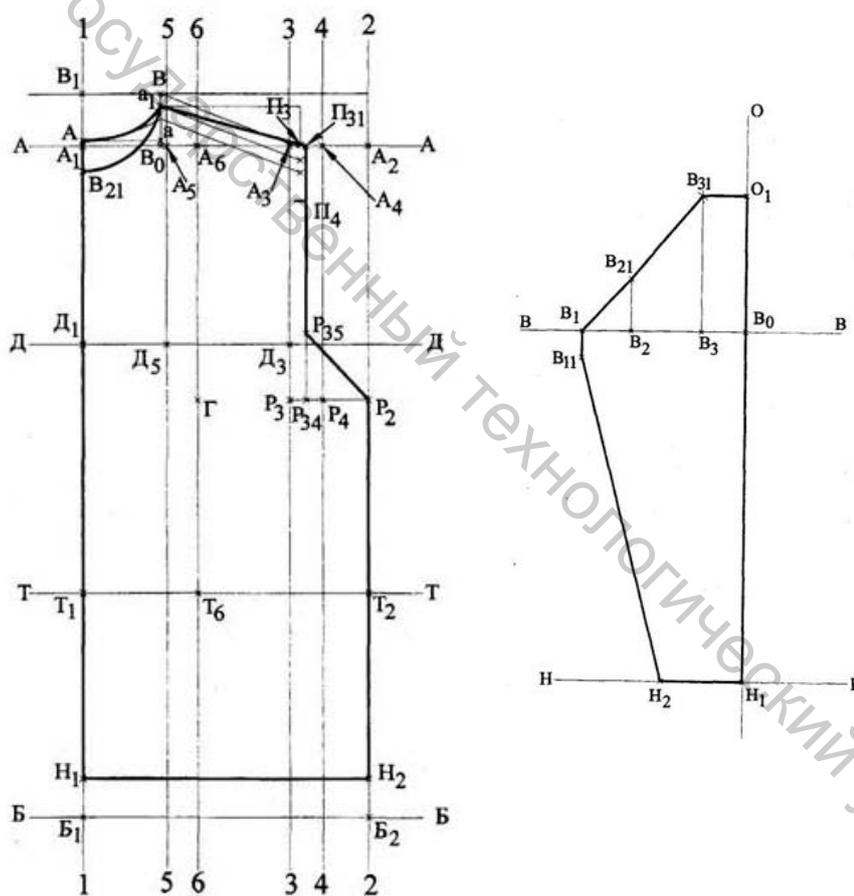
Чертеж конструкции стана и рукава регулярного изделия
